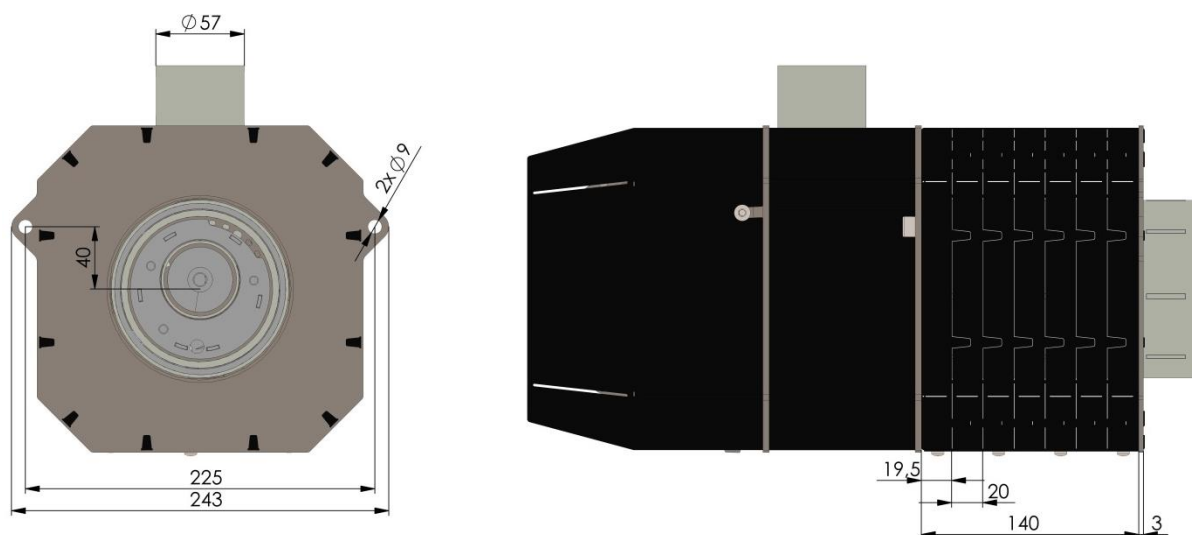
Zobrazení hořáku 4-16 kW s izolačním pláštěm a montážní přírubou
